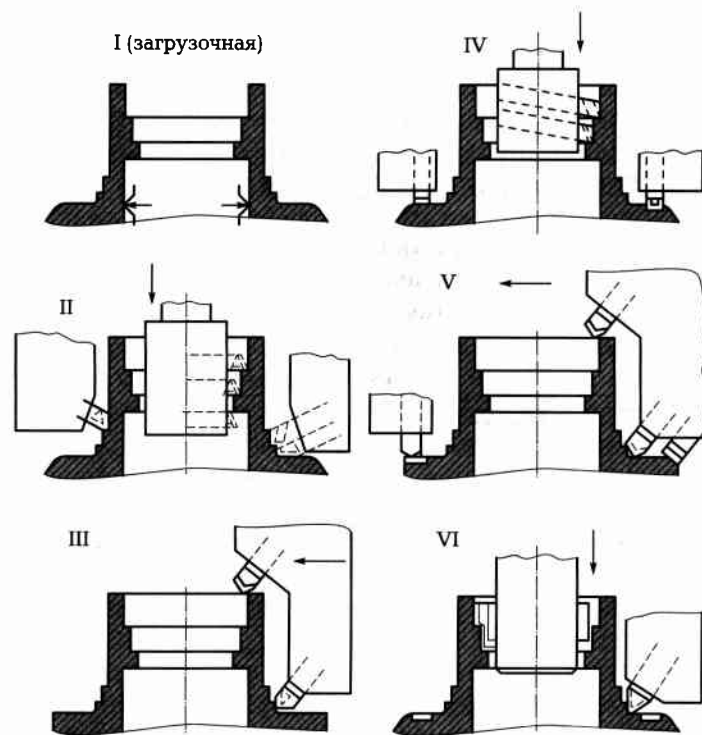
Технологическая схема обработки заготовки на вертикальном шестипозиционном полуавтомате
